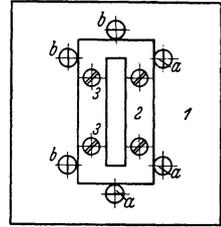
Zentrieren der Schnittplatte durch Klemmstifte. 1 Grundplatte. 2 die darin eingesenkte Schnittplatte. 3 Befestigungsschrauben. a Kupfer. b Splinteisen.
